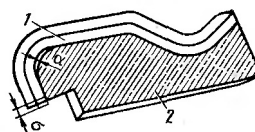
Универсально-сборное приспособление для изготовления и контроля деталей из труб по первой группе точности
